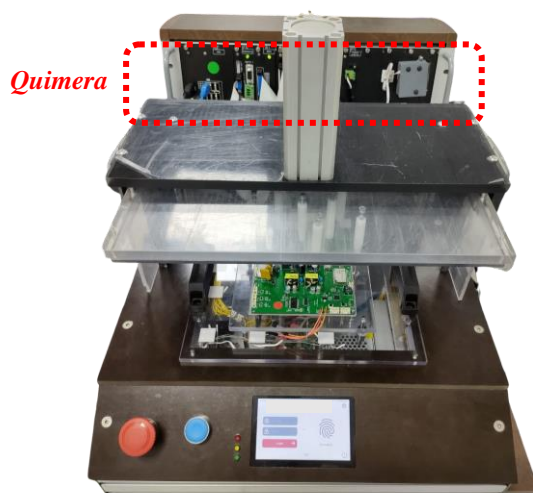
Integração da plataforma Quimera em um sistema de teste de PCB
